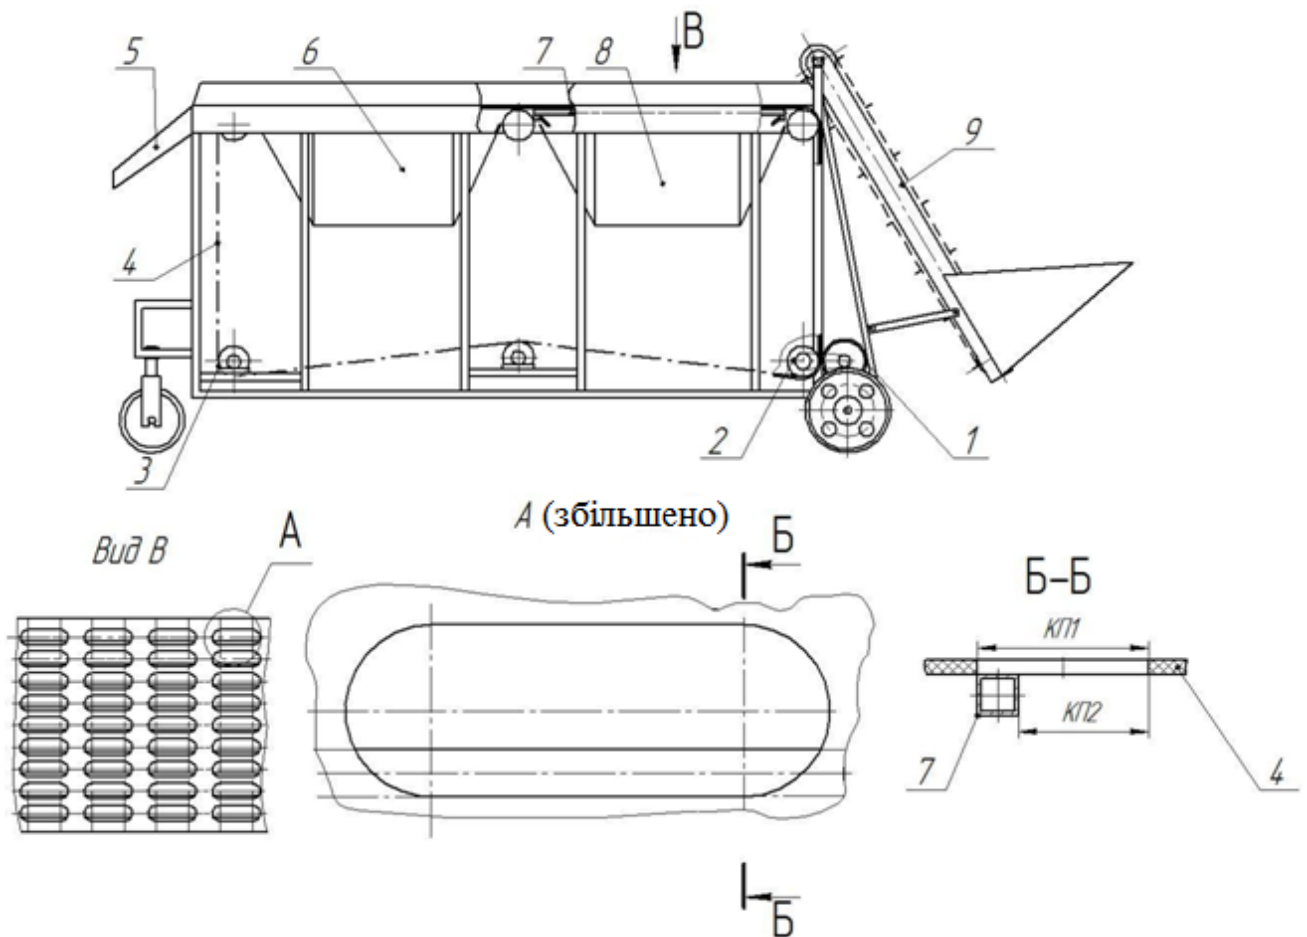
Принципова схема сортувального пристрою: 1 – приводний мотор-редуктор; 2 – ведучий барабан; 3 – підтримувальний барабан; 4 – транспортерна стрічка; 5 – лоток приймання великої фракції; 6 – лоток приймання середньої фракції; 7 – калібрувальне решето; 8 – лоток приймання дрібної фракції; 9 – транспортер для подачі з приймальним лотком.
